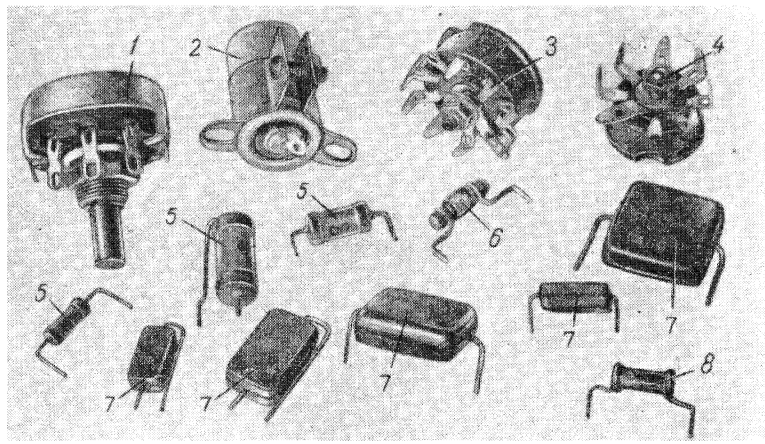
Детали, приспособленные для монтажа на печатной плате.
